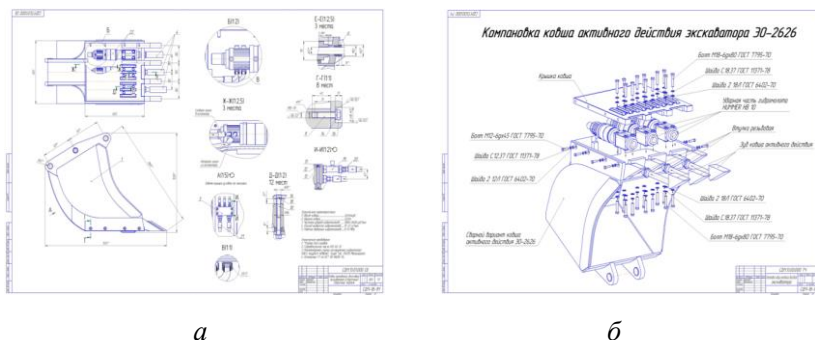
Сборочный чертеж (а) и 3D-компоновка (б) ковша с тремя малогабаритными гидроударными элементами, встроенными параллельно с существующими зубьями
